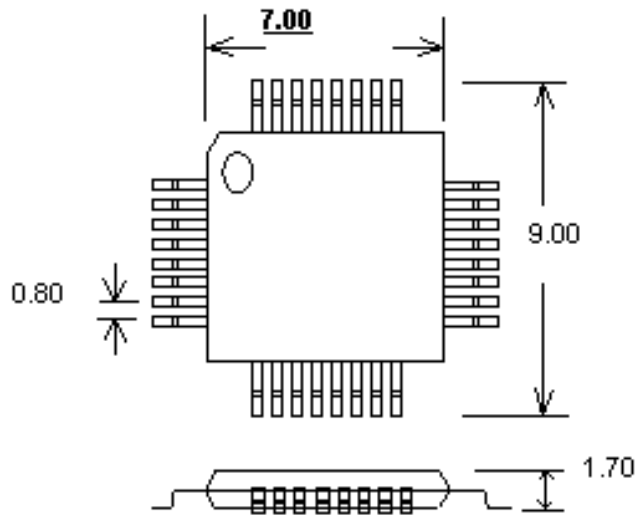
Габаритні розміри SMD корпусу TQFP-32
